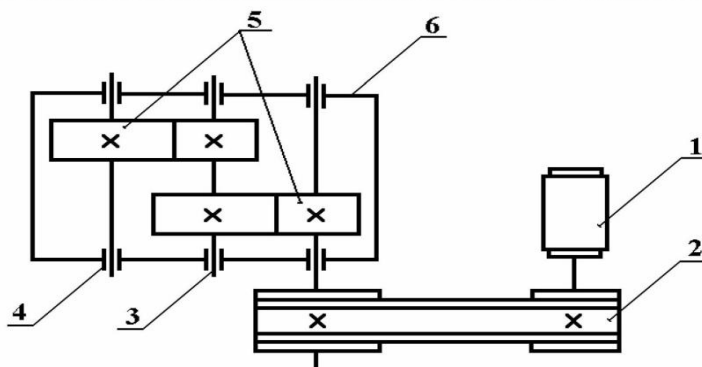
Кинематическая схема привода с цилиндрическим зубчатым редуктором:
